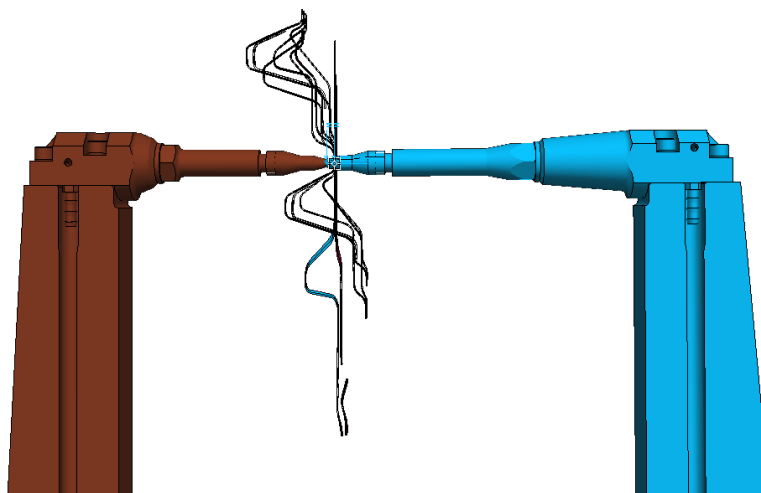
Сечение точек контакта сварочного пистолета и автодетали
